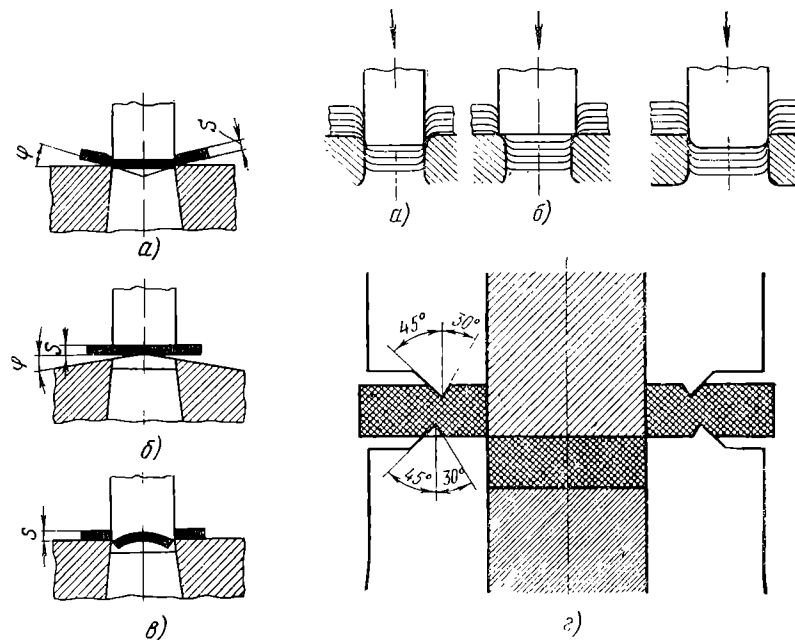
Вырубka и пробивка в штампах с наклонными режущими кромками:
